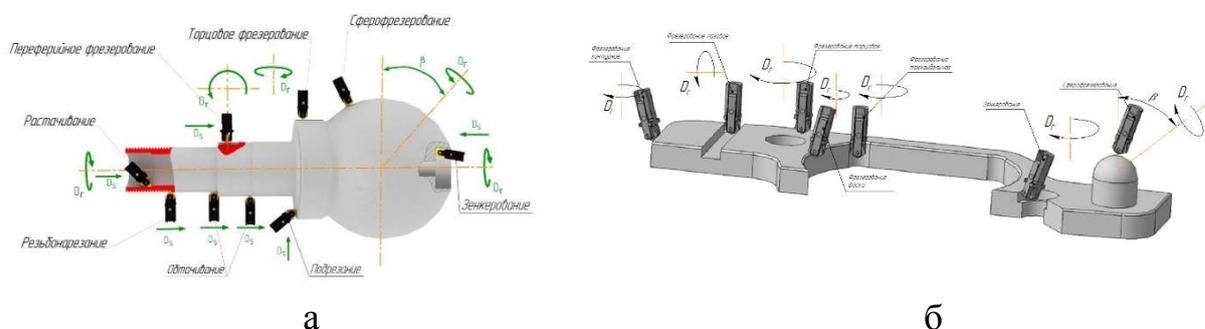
Схема обработки комплексной детали с использованием многофункциональной технологической оснастки: а – на токарном станке с ЧПУ; б – на фрезерном станке с ЧПУ
